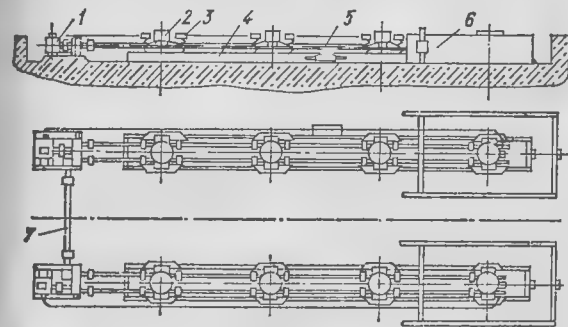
Схема виброплощадки конструкции Гипростроммаша:
